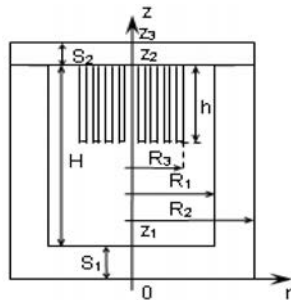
Схема сталеразливочного ковша с электронагревателем
